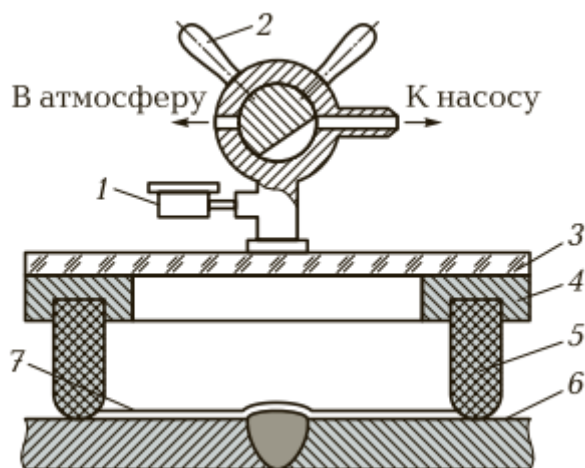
Схема контроля герметичности с помощью вакуумной камеры: 1 – вакуумметр; 2 – трехходовой кран (в двух положениях); 3 – иллюминатор из оргстекла; 4 – металлическая рамка; 5 – уплотнитель (присоска) из губчатой резины; 6 – контролируемое сварное соединение; 7 – пленка пенообразующего вещества
